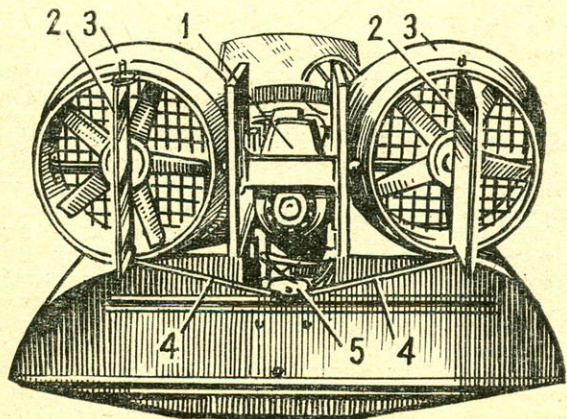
Общий вид винтомоторной установки с кормы: 1 — двигатель «Ллойд» 24 л. с., 2—2 — воздушные рули, 3—3 — аэродинамические кольца, 4—4 — рулевые тяги, 5 — рулевой шкив.
